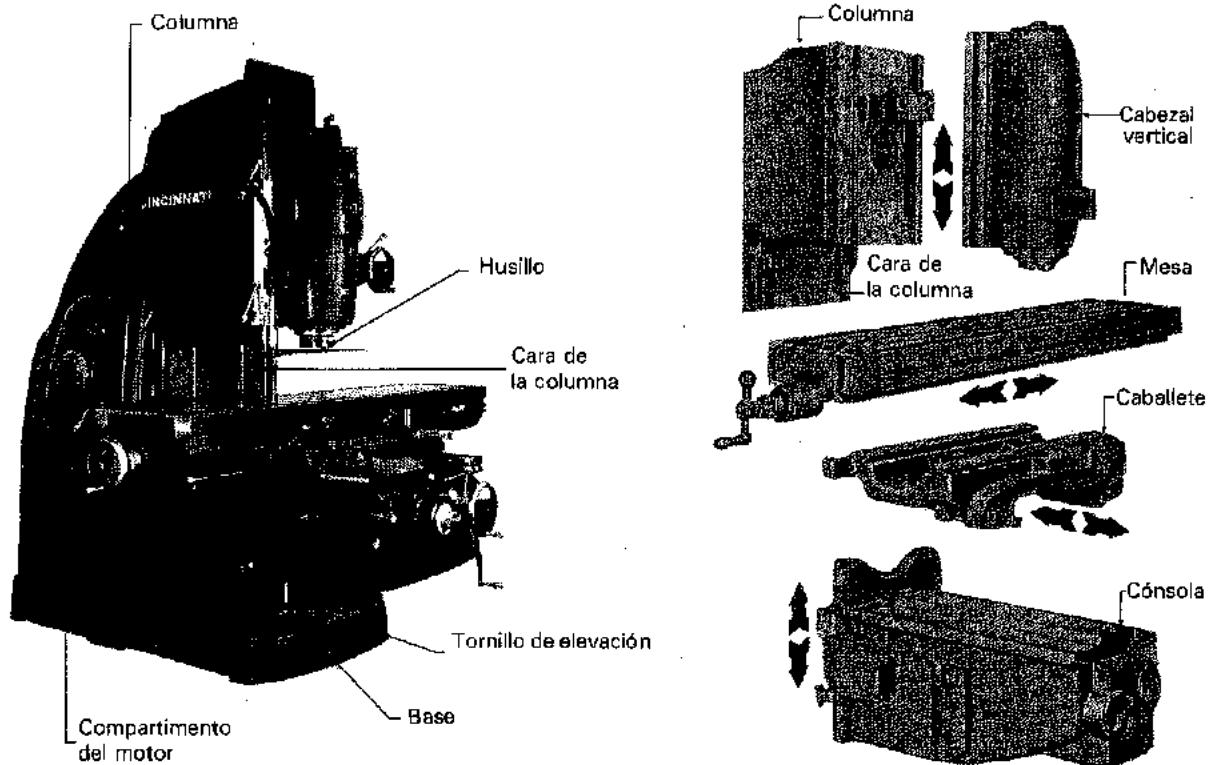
Elementos principales de la fresadora vertical del tipo de columna y cartela (Cincinnati Milling Machine Co.)
